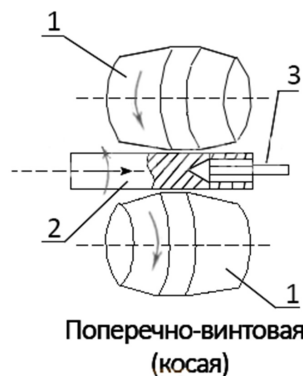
Схема двухвалковой ПВП: 1 – валковая пара; 2 – тело заготовки; 3 – гильза.
